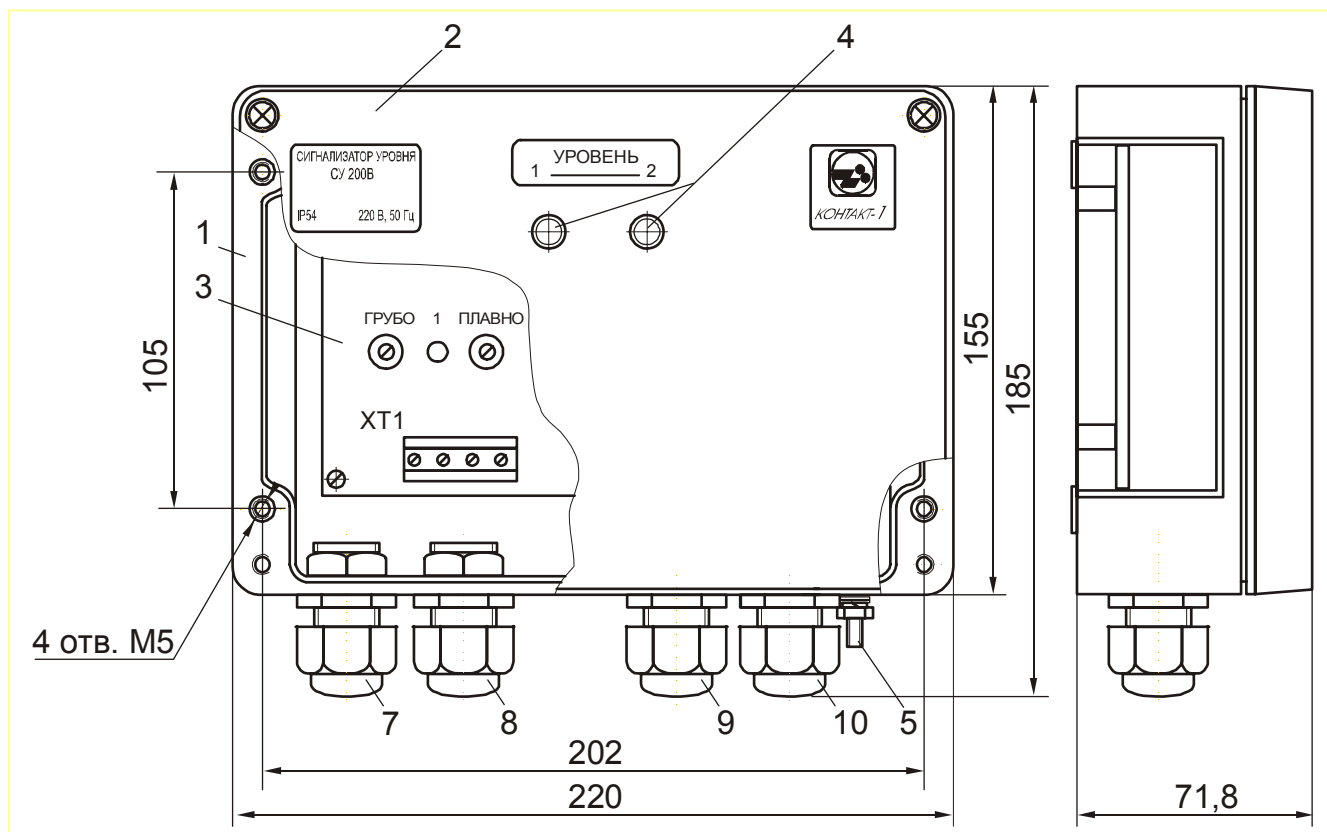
Внешний вид, габаритные и установочные размеры вторичного преобразователя
